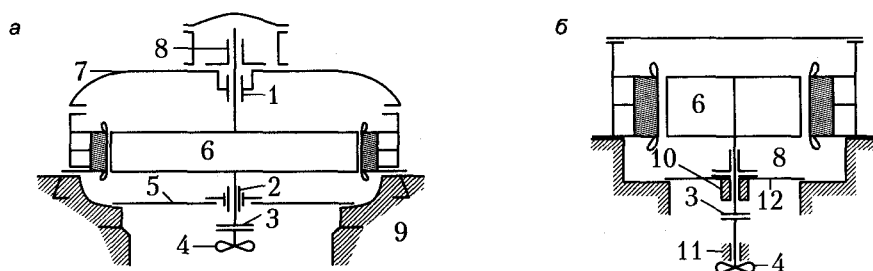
Конструктивные схемы вертикальных гидрогенераторов: а — подвесного; б — зонтичного исполнения: 1 — верхний направляющий подшипник; 2 — нижний направляющий подшипник; 3 — фланец вала; 4 — турбина; 5 — нижняя крестовина; 6 — ротор; 7 — верхняя крестовина; 8 — подпятник; 9 — фундамент; 10 — направляющий подшипник; 11 — направляющий подшипник турбины; 12 — нижняя крестовина
